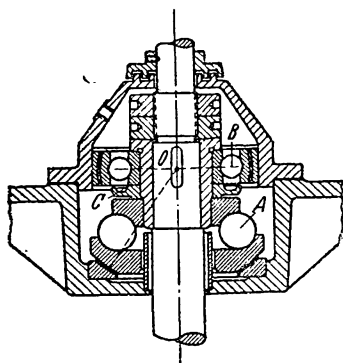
Комбинированный радиальный и упорный подшипник для двухстороннего давления.
